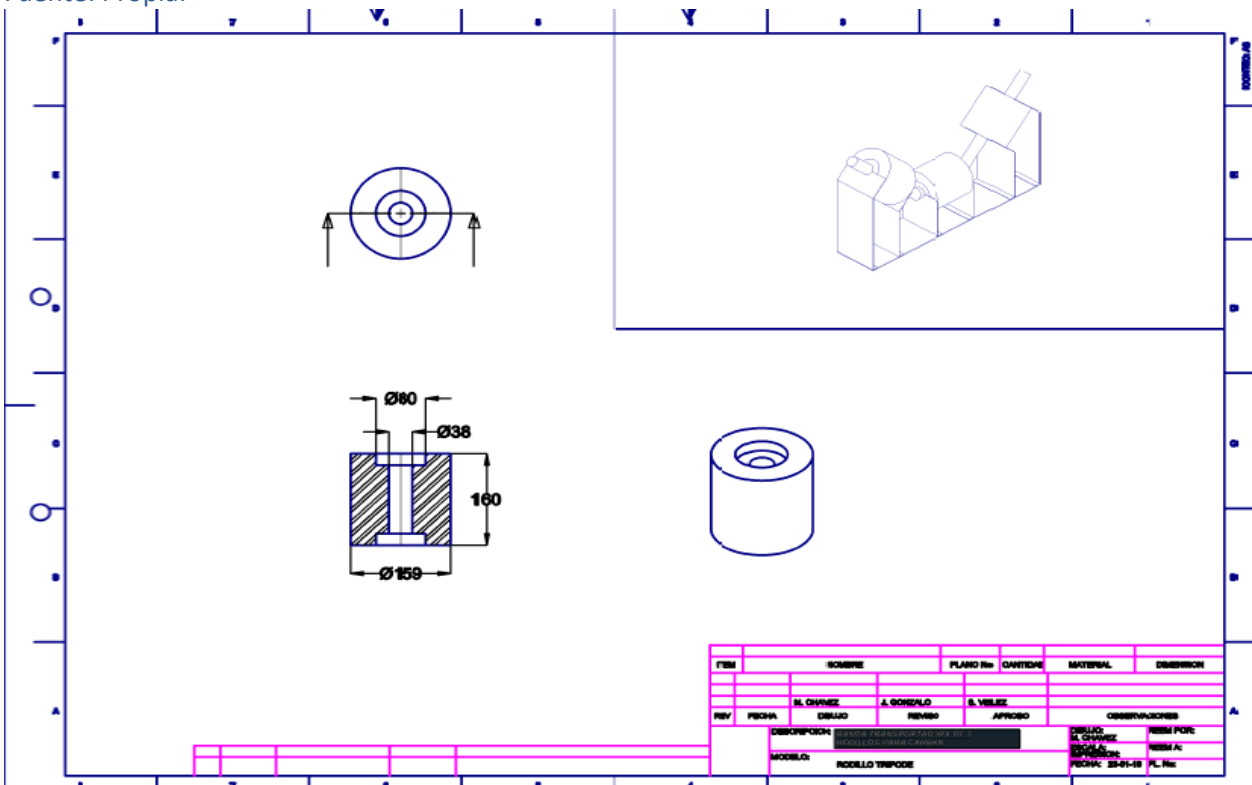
Plano detallado del orificio ocupado por el rodamiento en el sistema de banda.
